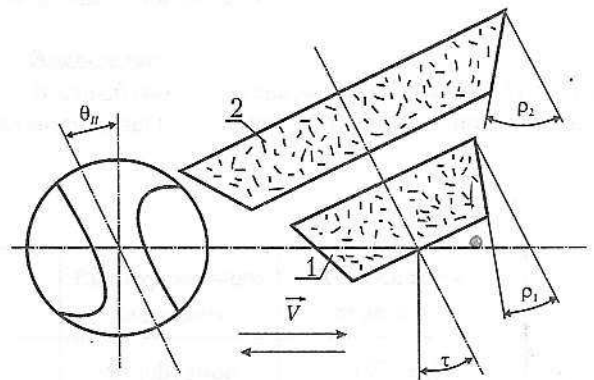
Схема образования задних поверхностей сверла двумя шлифовальными кругами
